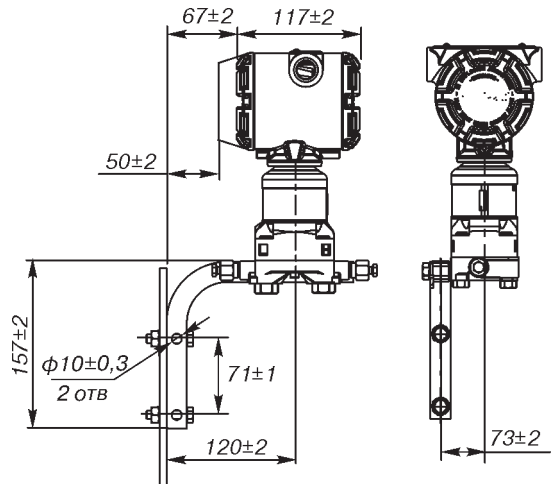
Монтаж на панели (стене) датчиков расходомеров типа SFA.
